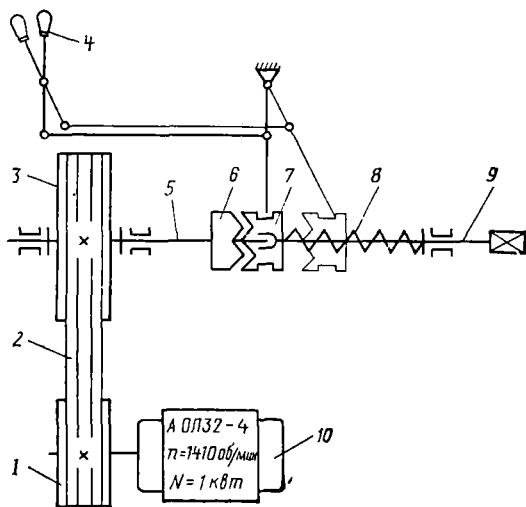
Гайковерт для гаек колес грузовых автомобилей:
